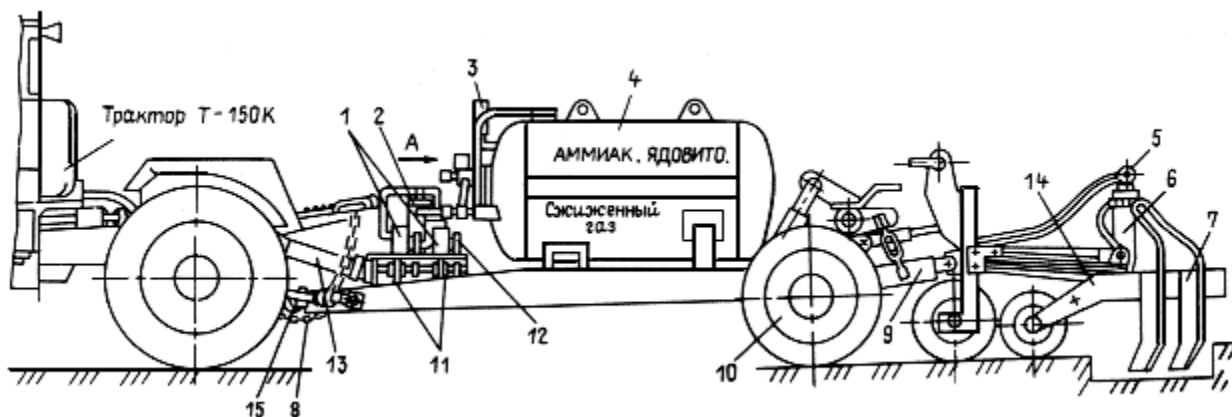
Агрегат безводного аммиака АБА-1-150К: 1 - трактор Т-150К; 2 - сосуд (2 шт.); 3 - рама агрегата; 4 - культиватор КРН-8,4 (или плуг ПЛН-5-35); 5 - дозатор объемный; 6 - клапан отсечной; 7 -
